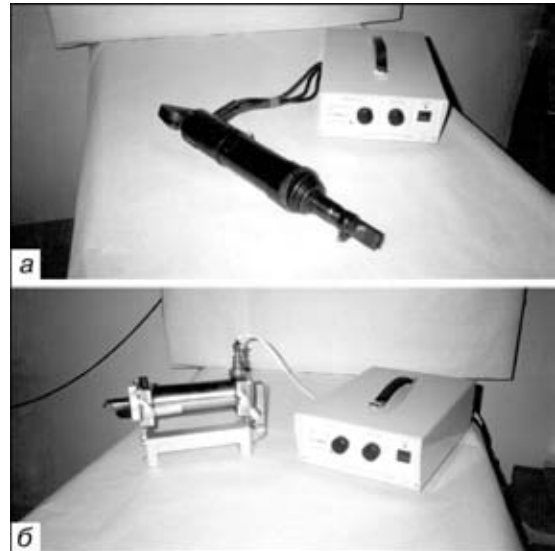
Установка для упрочняющей обработки сварных соединений на ультразвуковой частоте: *a* — ультразвуковой молоток; *b* — ударное устройство для обработки поверхности деталей трением
